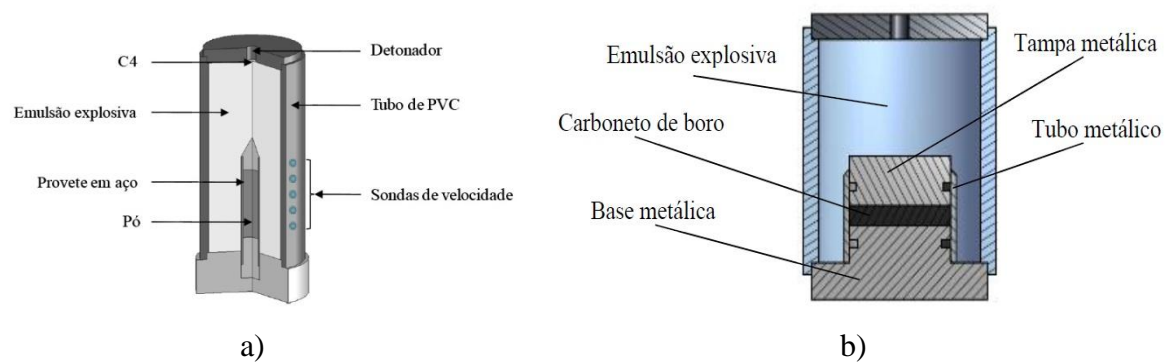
Configurações de detonação: a) Configuração cilíndrica [4]; b) Configuração plana [3]
